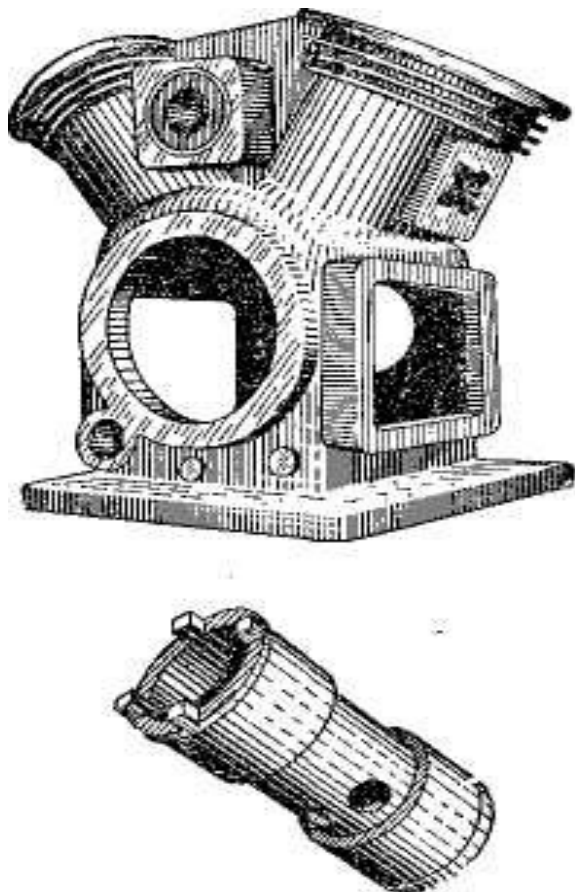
Блок картера У-образного четырёхцилиндрового компрессора и его цилиндровая гильза
